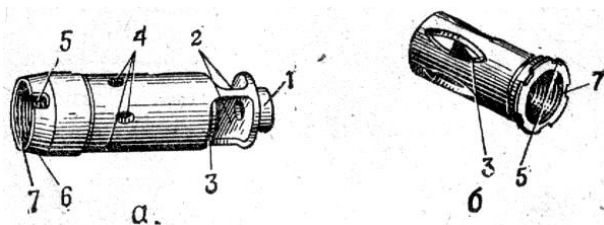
Дульный тормоз-компенсатор и пламегаситель:
